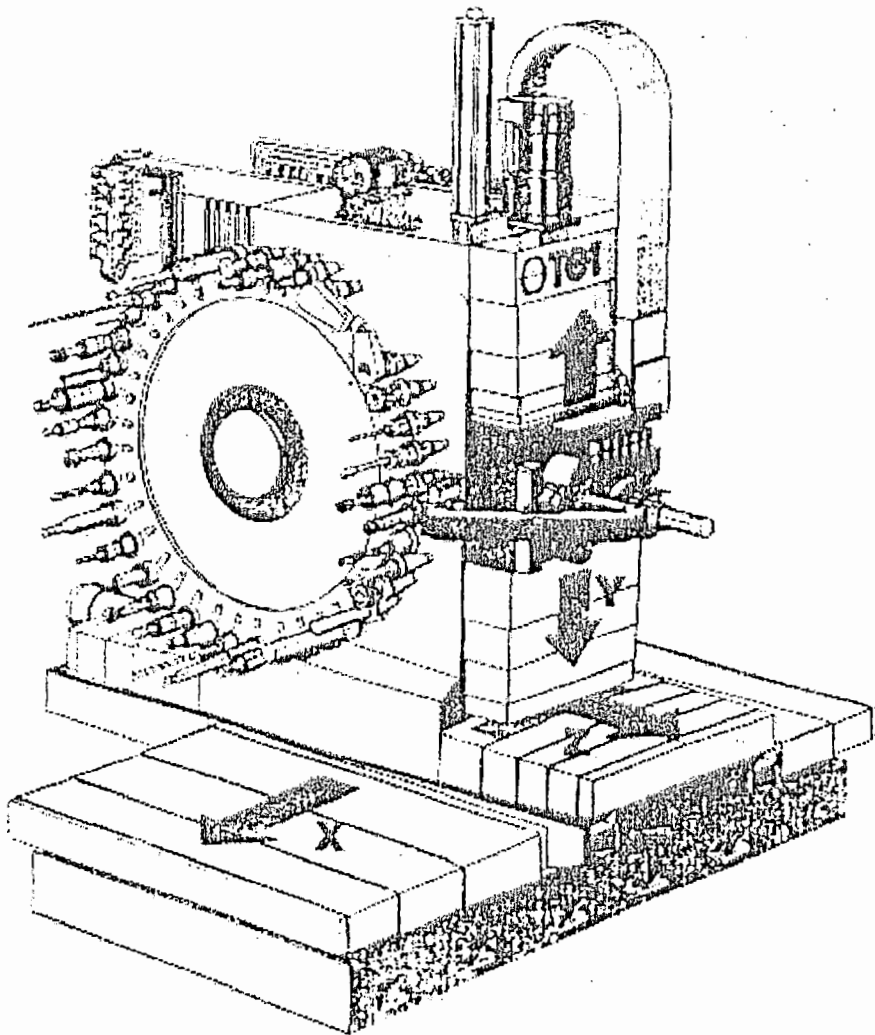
Centro de usinagem CNC horizontal com magazine de ferramentas para troca automática.
